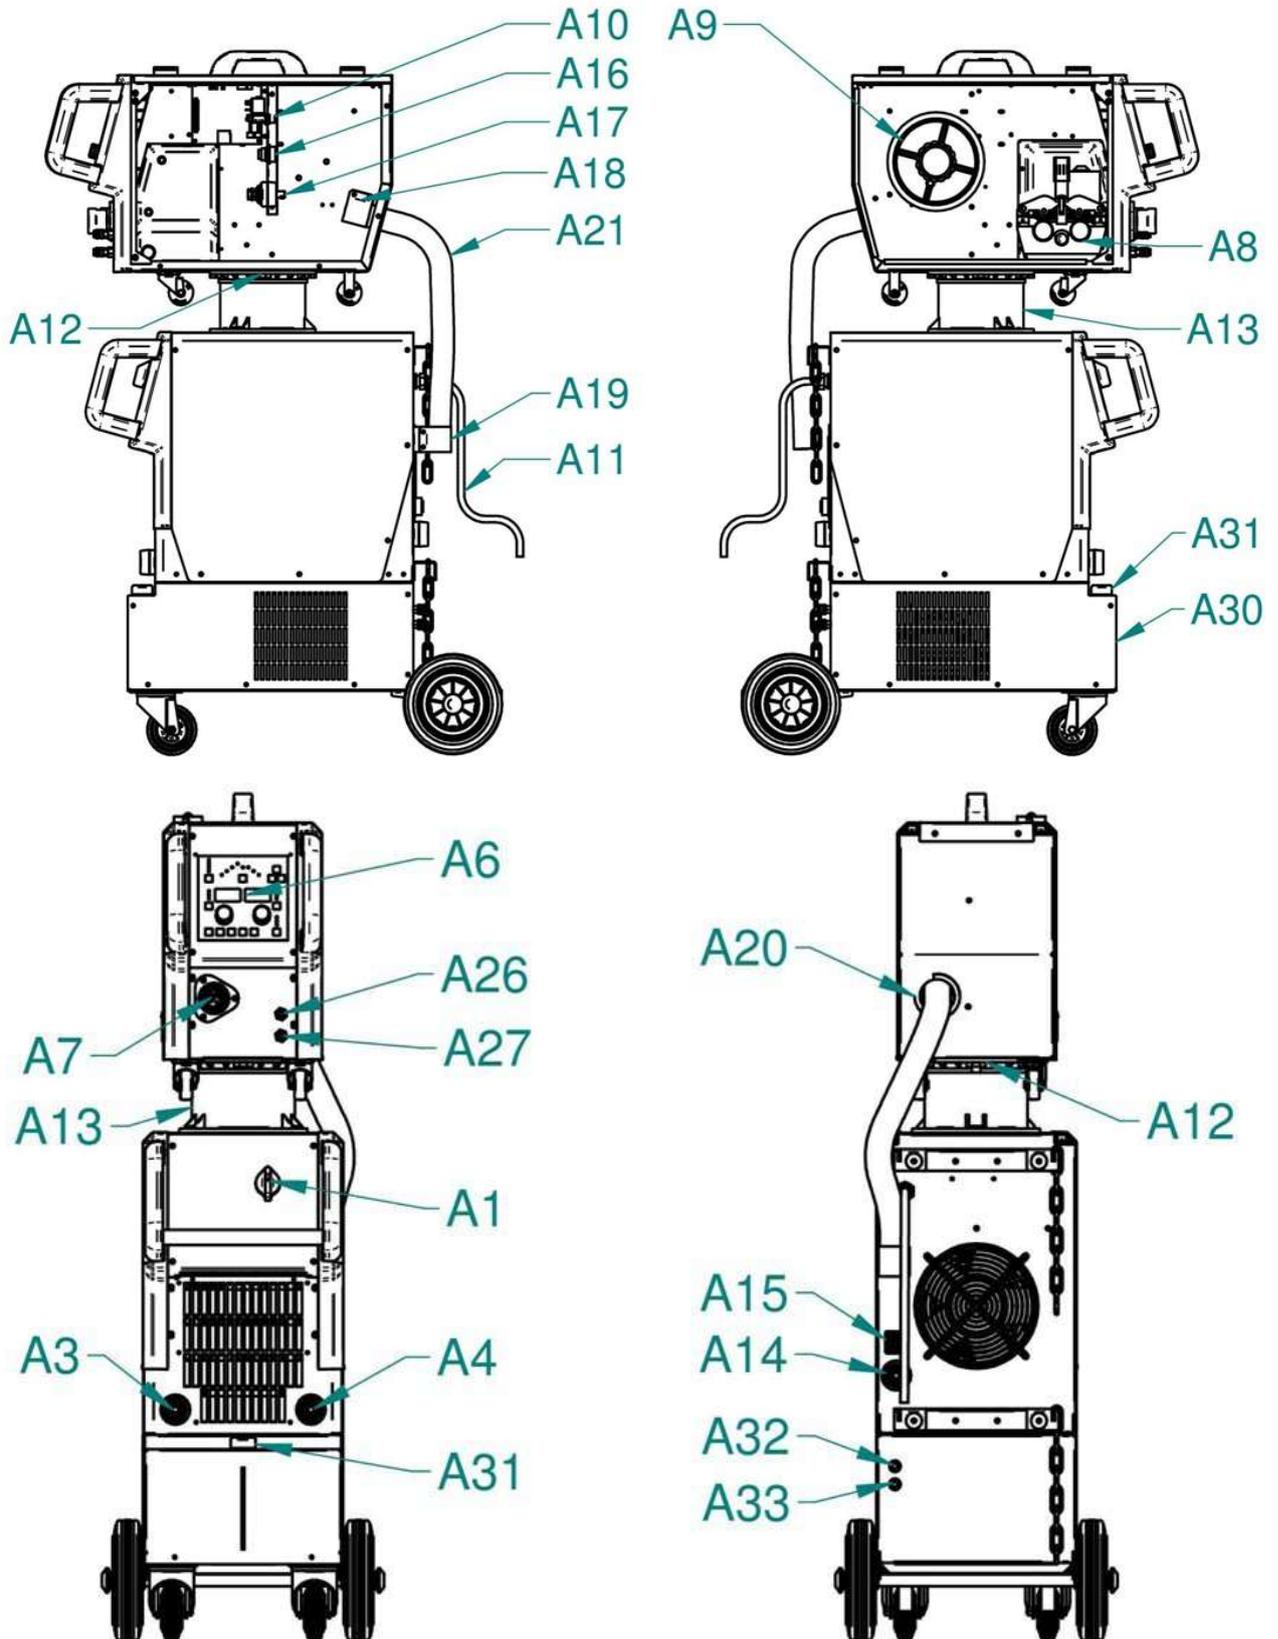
Hauptteile der Maschine aXe 400/500 IN
